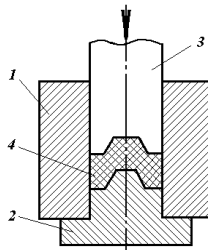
Схема компресійного пресування: 1 – матриця;
